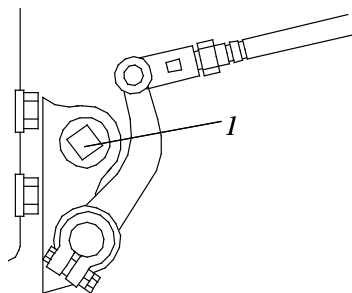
Резьбовое отверстие смазки подшипника отводки сцепления:
